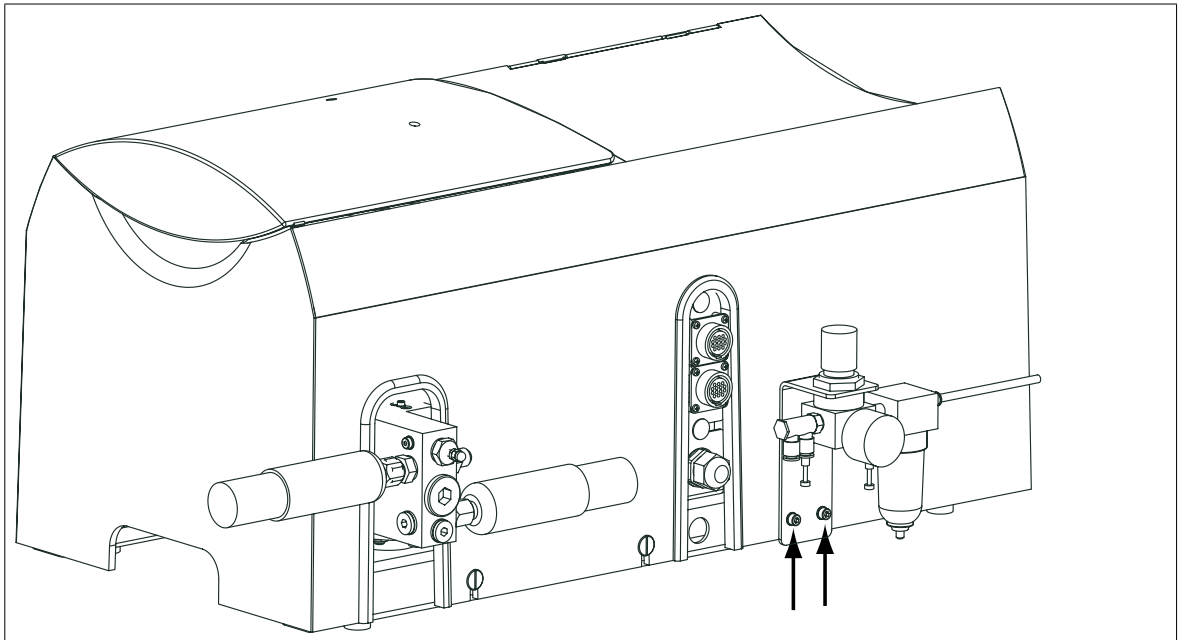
/1: Montage van de persluchtunit voor spraylucht
